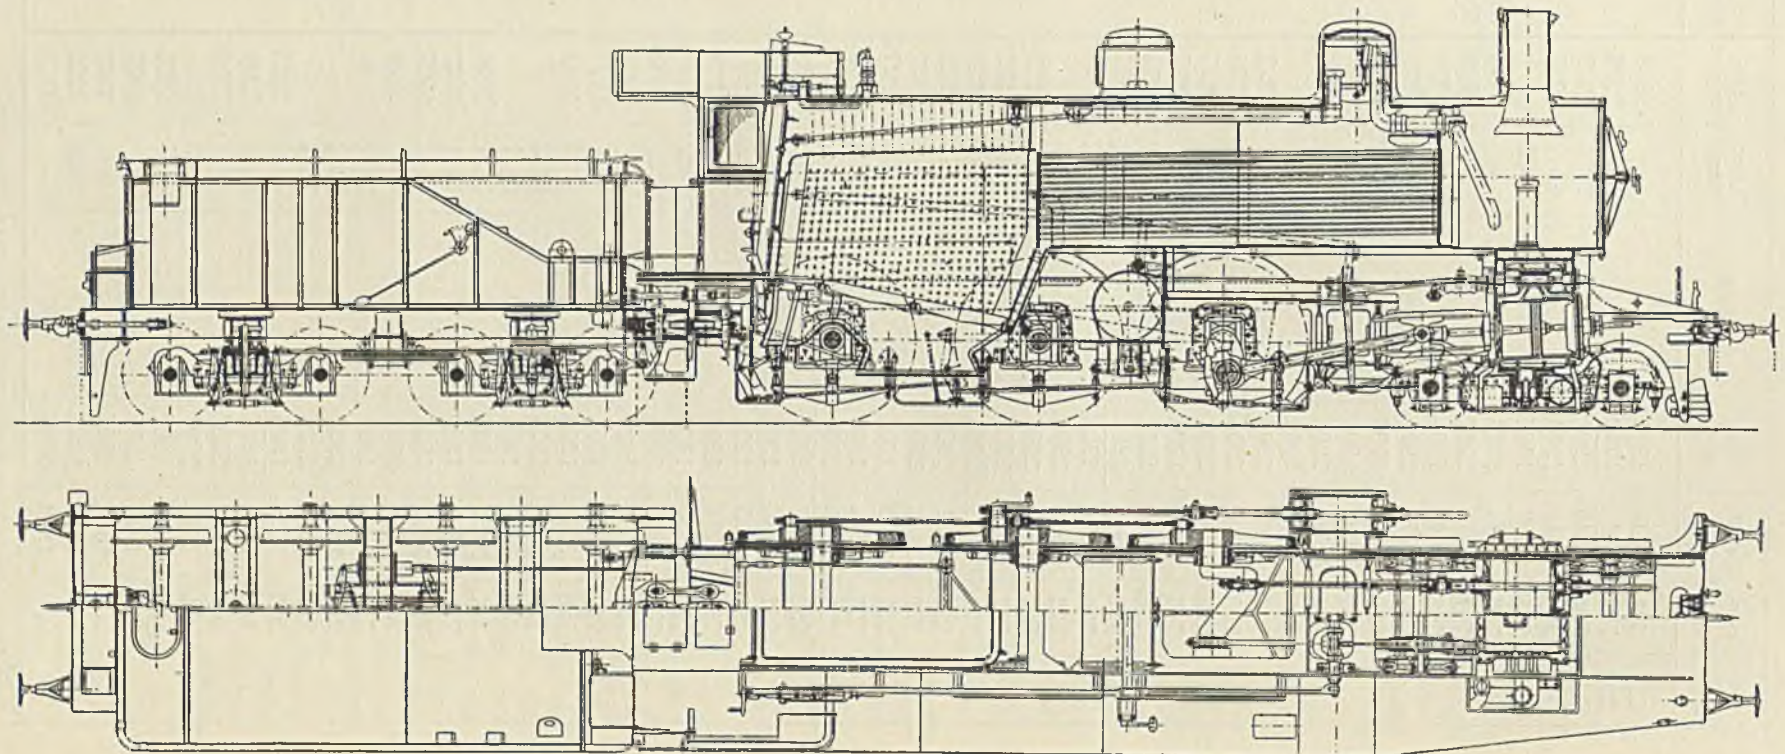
Längsschnitt. Abbildung 193a: $\frac{1}{2}$ -Wagrechtschnitt, $\frac{1}{2}$ Grundriss.
